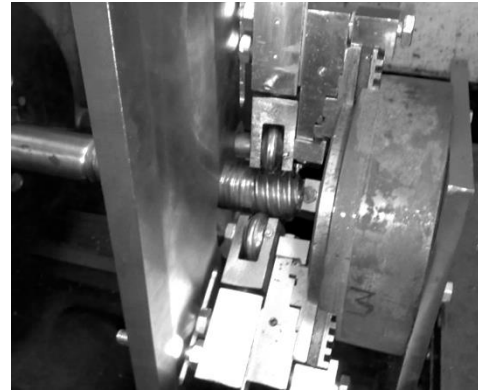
Трьохроlikова обkочувальна головка, встановлена на токарно-гвинторізний верстат
